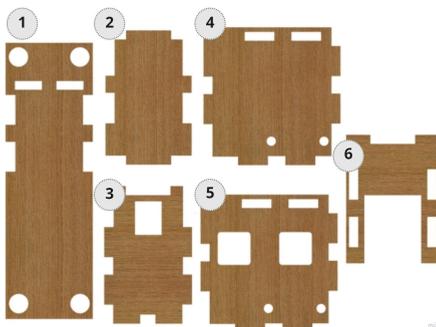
Elementos estruturais módulo Motor DC. Fonte: A autora.
